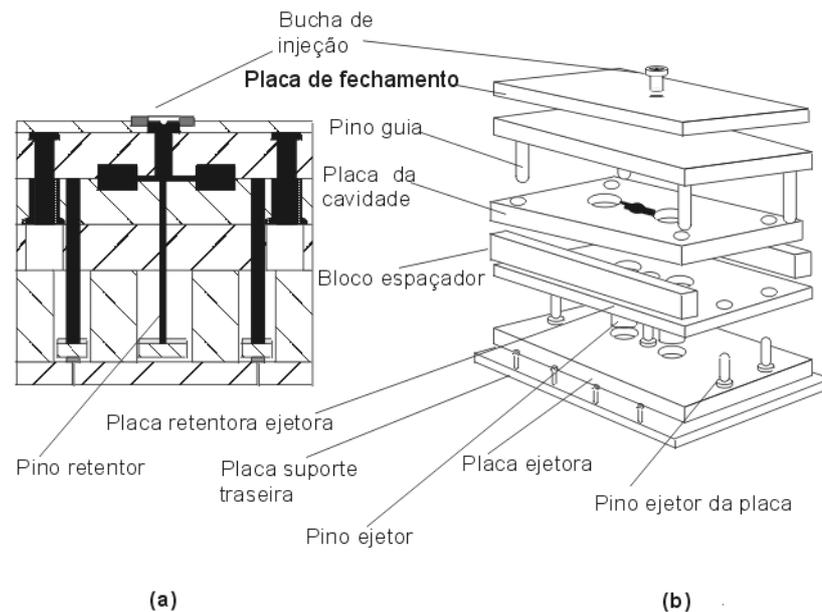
Molde de injeção complexo. a) Vista em corte, b) Vista explodida.
